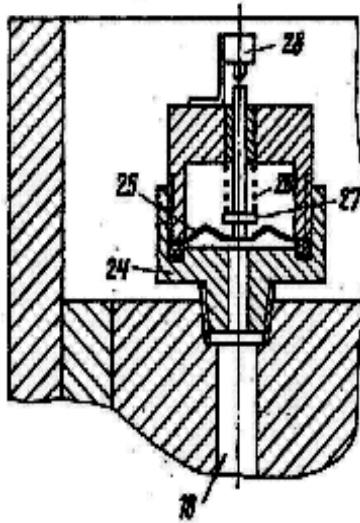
Розріз Б-Б (рис.1.9)
